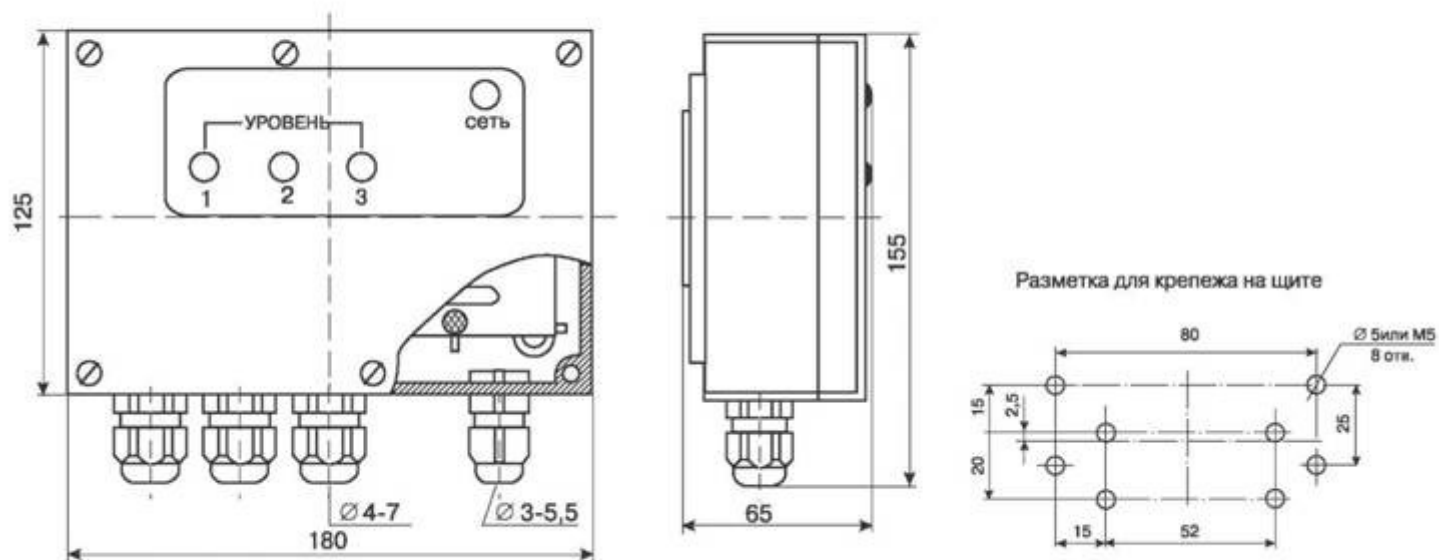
Габаритные и установочные размеры преобразователя передающего ДРУ-ЭПМ (ПВ-2)
